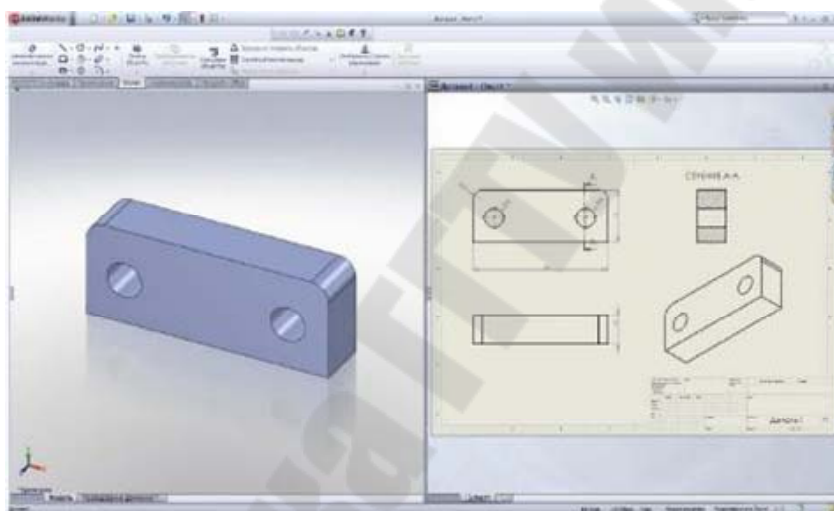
Конструкторский чертеж, ассоциативно связанный с геометрической моделью
